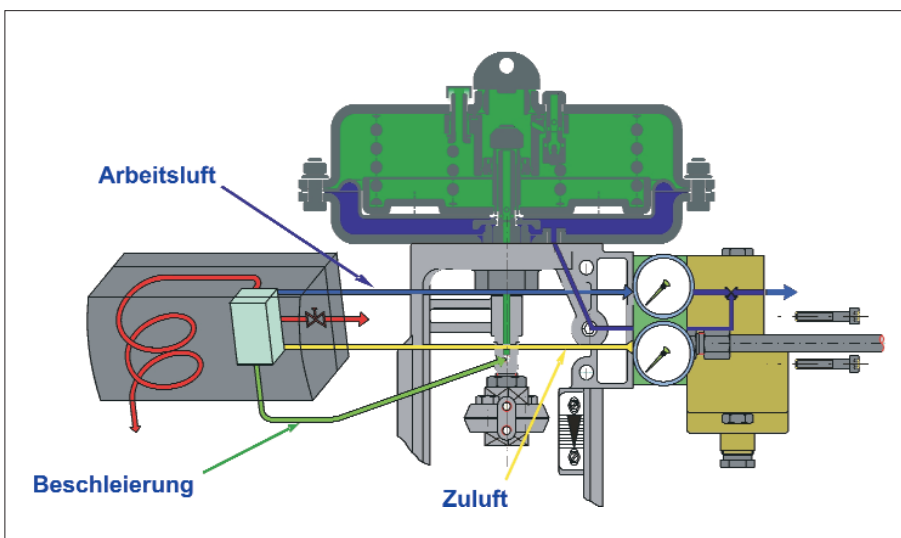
Beschleierung des Stellantriebes mit Instrumentenluft
